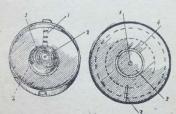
а) пижний диск магазина: 1—аоток; 2—втулка; 6) верхний диск магазина: 4—обруд. 6) верхний диск магазила: 1—отверстие для втулки; 2—стойка; 3—задержка заподной пружины; 4—зубъя для помещения патроном
